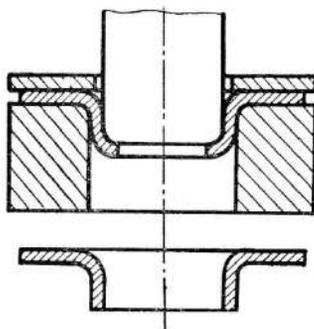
Схема процесса отбортовки и готовая деталь
